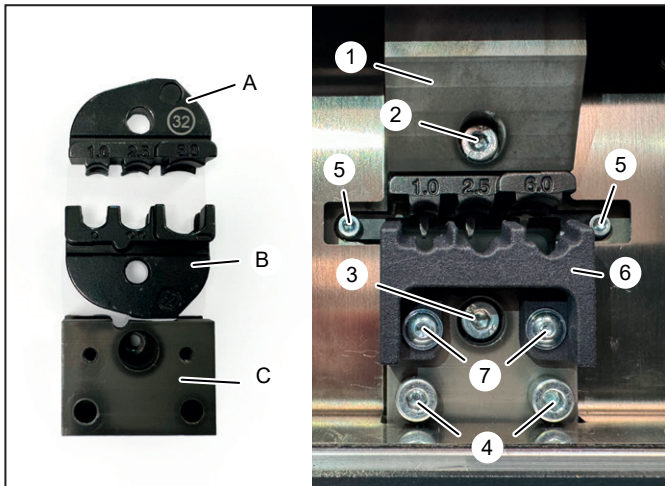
Crimpeinsatz für Kabelschuhe und Einlagehilfe
